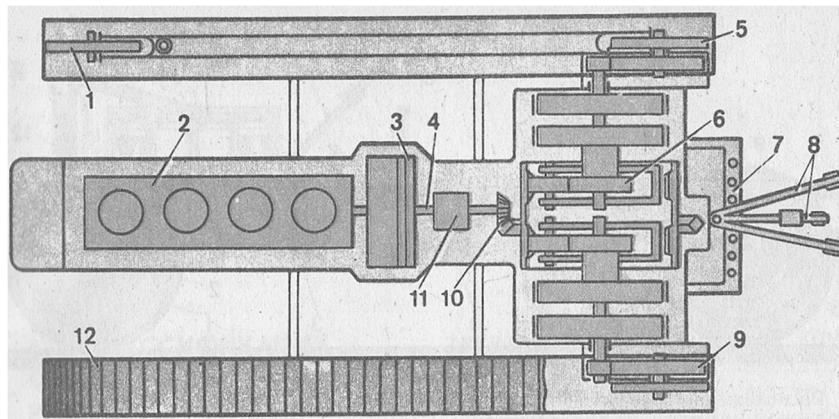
Розташування основних частин, їх механізмів і деталей гусеничного трактора: 1 – направляюче колесо; 2 – двигун; 3 – муфта зчеплення; 4 – сполучний вал; 5 – провідне колесо; 6 – планетарний механізм; 7 – причіпний пристрій; 8 – навісна система; 9 – кінцева передача; 10 – головна передача; 11 – коробка передач; 12 – гусеничний ланцюг.
